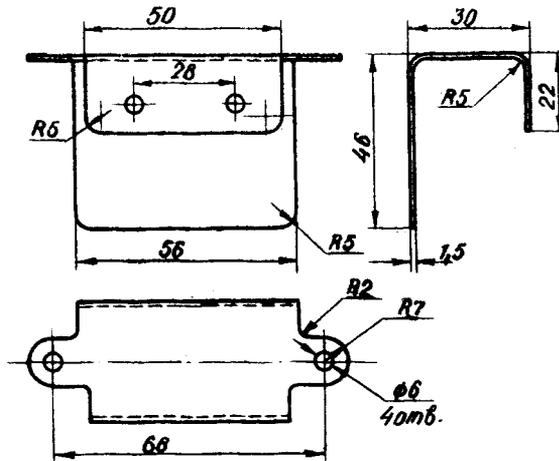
Деталь, полученная гибкой из листовой заготовки
